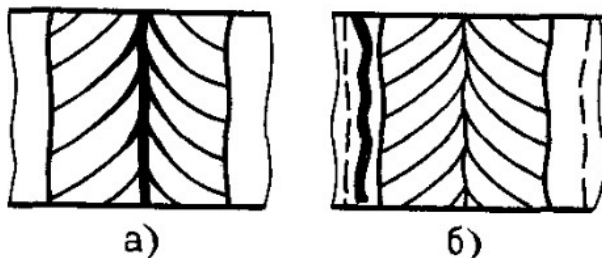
Виды трещин сварных соединений:
